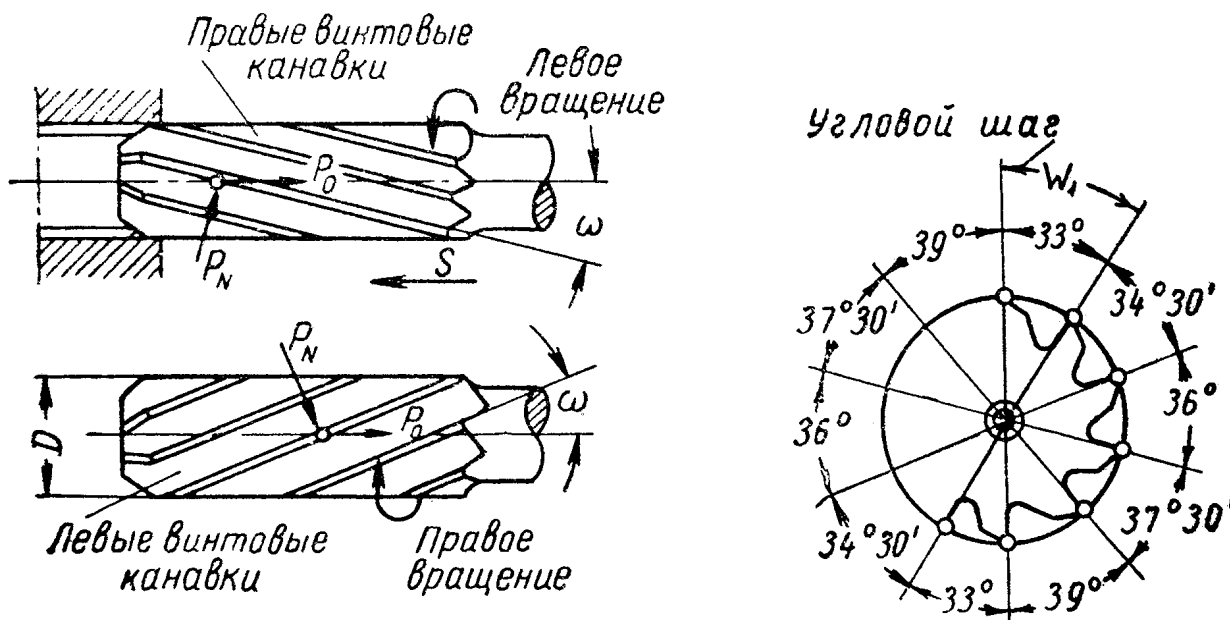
Развертки с различным направлением винтовых канавок и переменным угловым шагом зубьев
